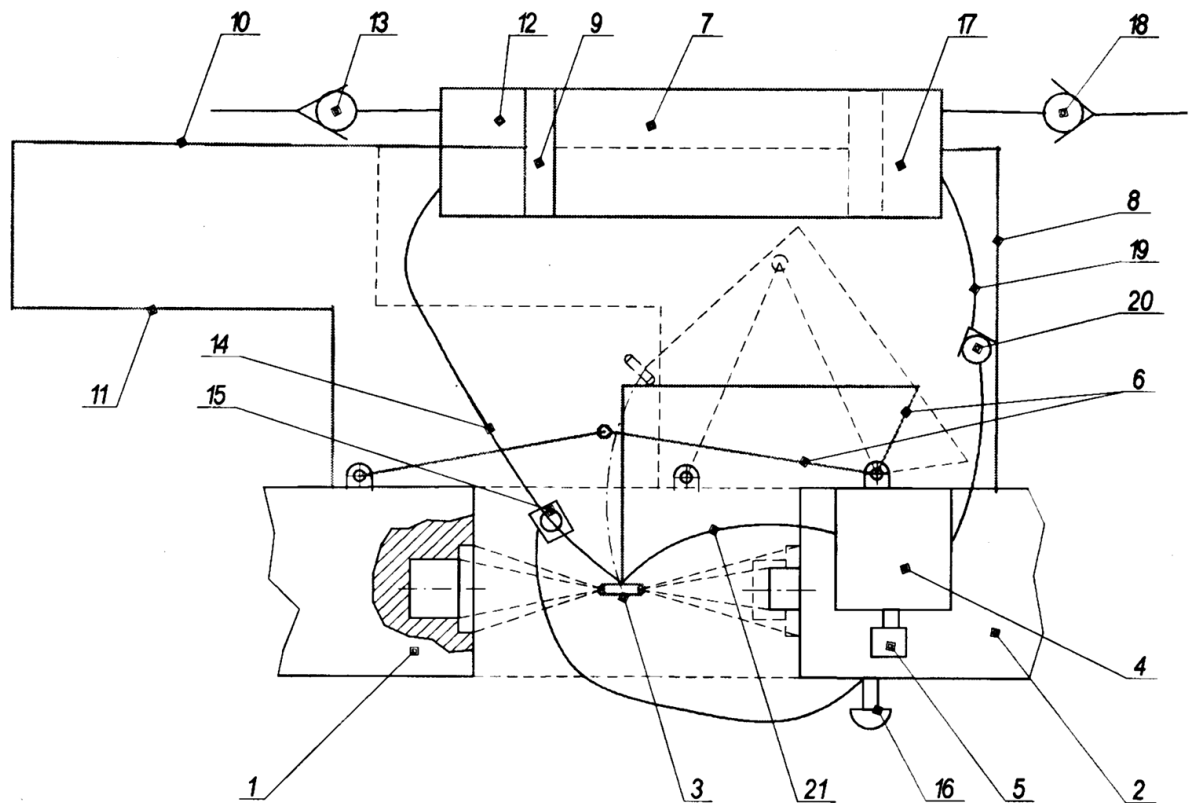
Схема автоматического манипулятора для смазки пресс-форм ЛПД
